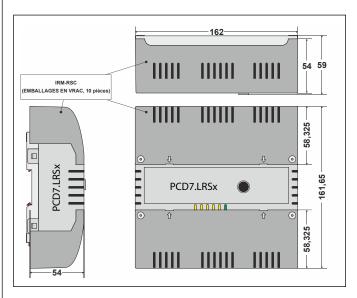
Grand boîtier, avec caches de protection des bornes, dimensions (en mm)
